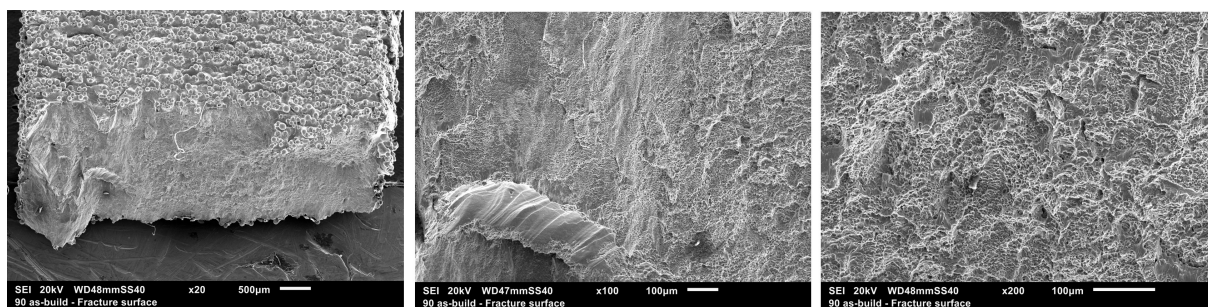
Superfície de fratura do corpo construído em 90° no seu estado primário aumentadas x20, x100 e x350. Fonte: Autor.
